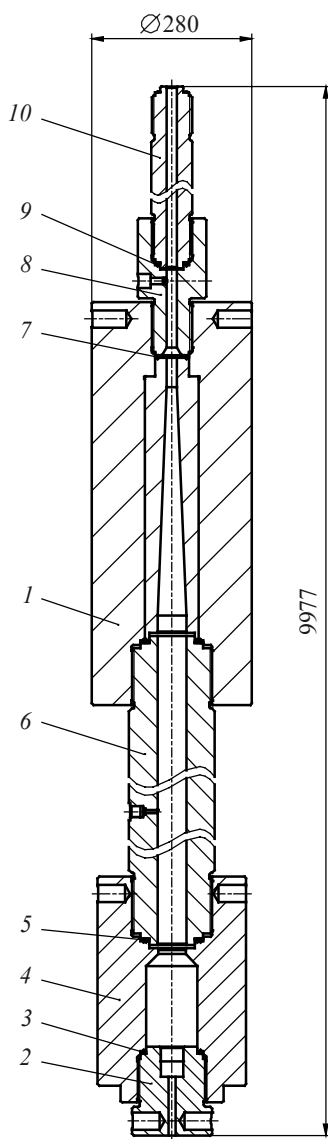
Сборочный чертеж двухступенчатой легкогазовой установки ГПМ (ППХ 50/18)
